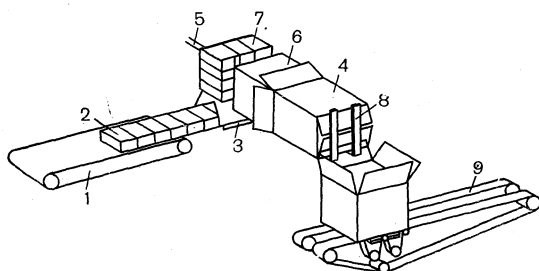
Схема групповой упаковки пачек в ящик. 1 — ленточный транспортер, 2 — пачка, 3 — подъемник, 4 — картонный ящик, 5 — направляющее устройство, 6 — поворотное устройство, 7 — блок пачек, 8 — платформа, 9 — ленточный транспортер.
